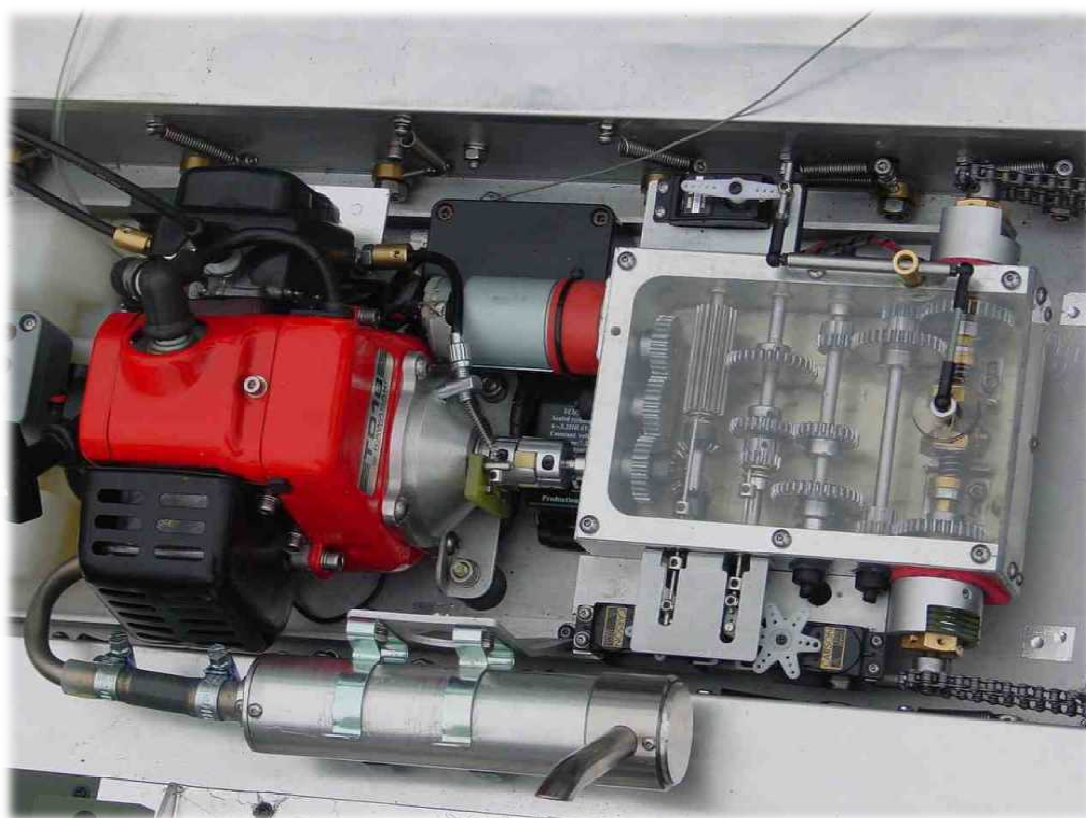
Skutečná zástavba benzínového motoru s převodovkou výrobce Ilja Cerjak
